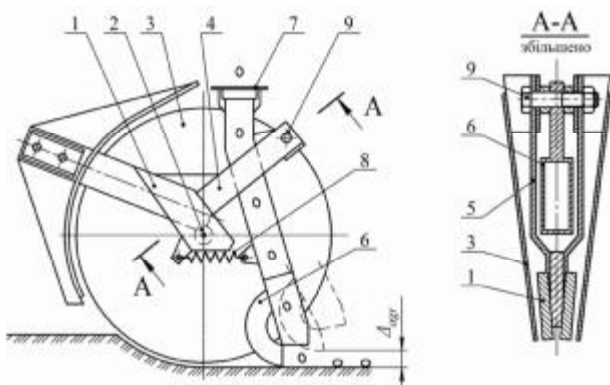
Конструктивно-технологічна схема комбінованого сошника (вигляд збоку при знятому лівому диску): 1 – корпус; 2 – вісь; 3 – диск; 4 – тримач; 5 – щока; 6 – розтруб; 7 – наральник; 8 – пружина; 9 – шарнірна підвіска
